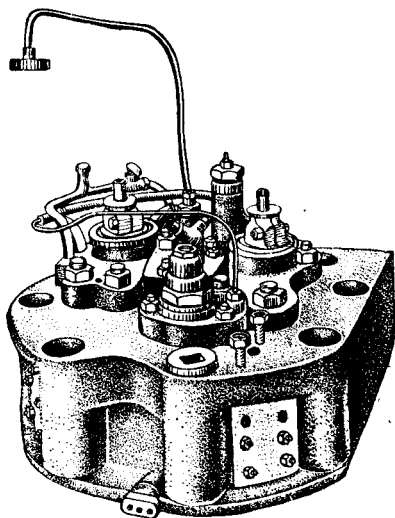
Цилиндровая крышка двигателя тепловоза Д5: 1—гнездо для установки форсунки; 2—тело крышки; 3—горловина вихревой камеры; 4—отверстие для шпильки крепления крышки; 5, 6—гнезда впускного и выпускного клапанов
